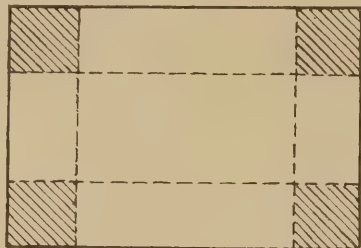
Zuschnitt für starre Schachteln mit Draht- oder Papierheftung.
